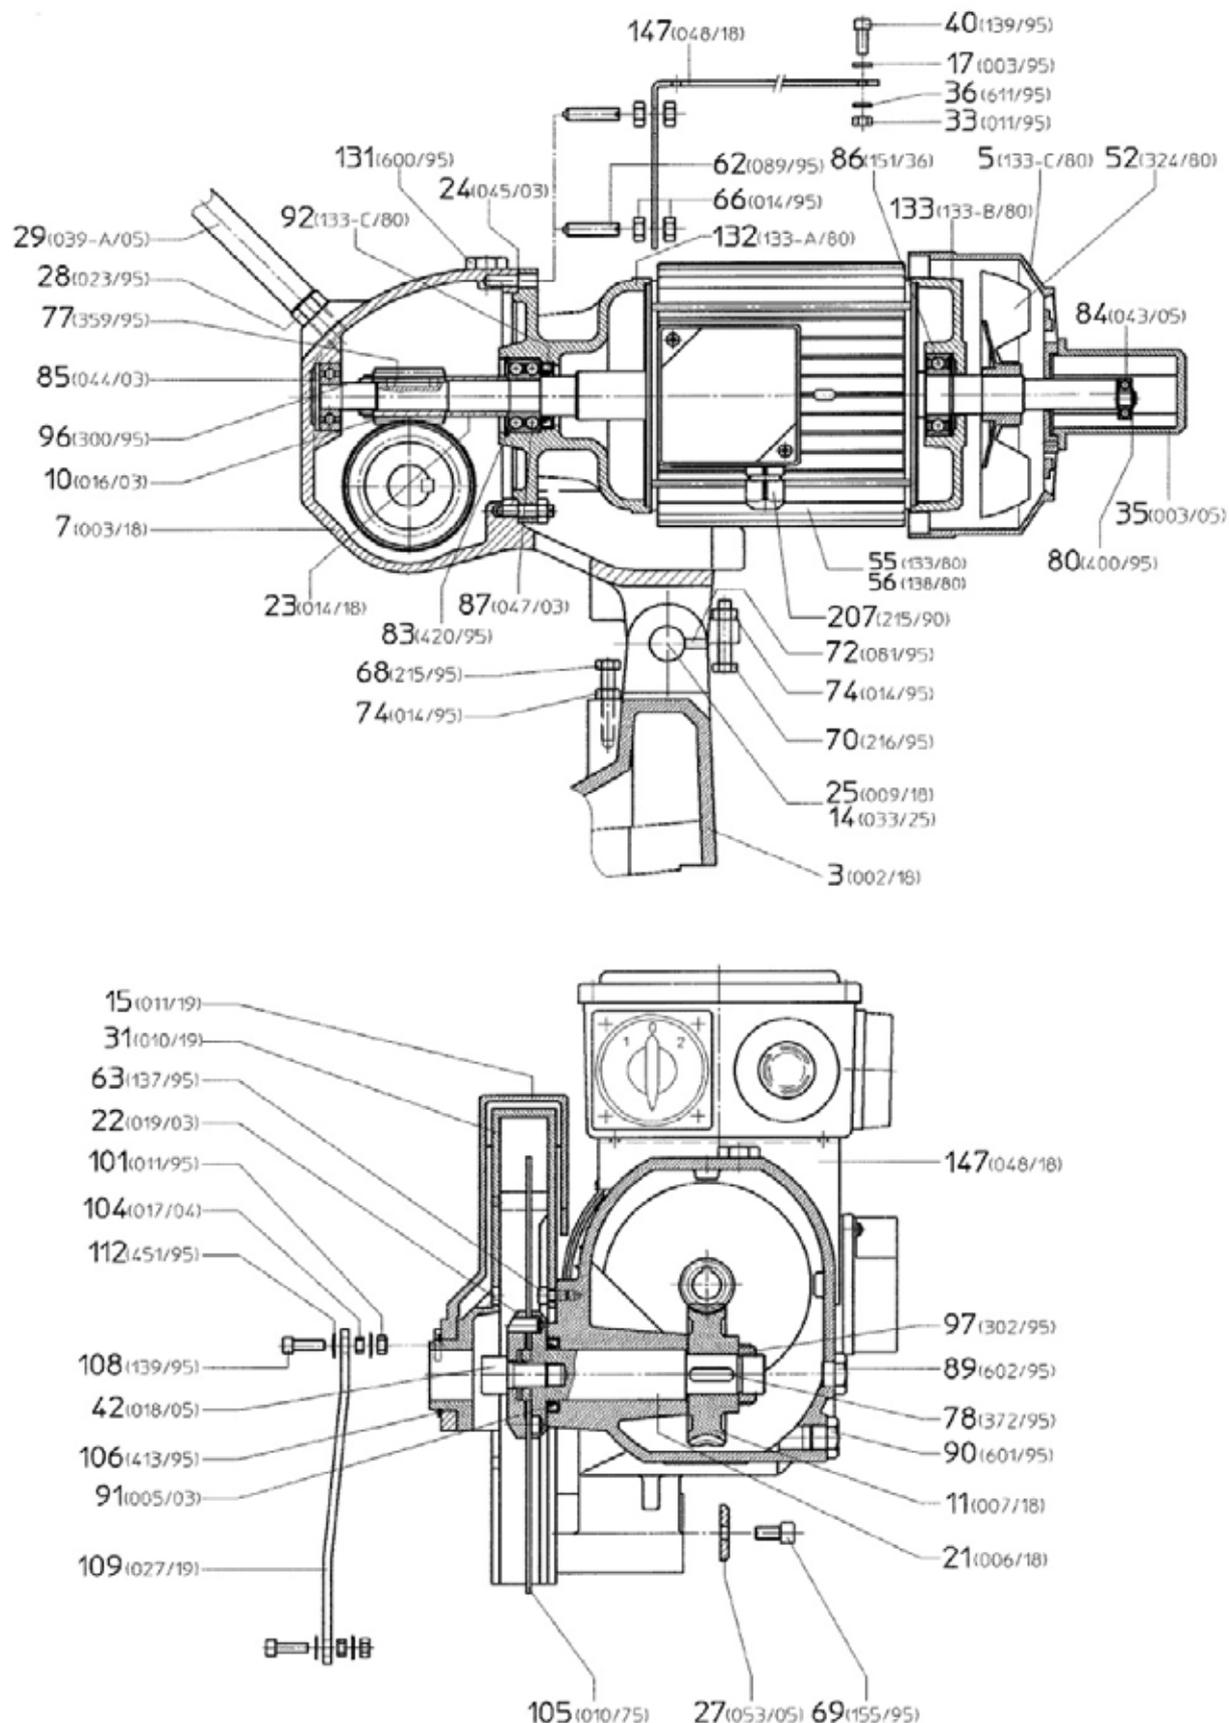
Dessin des pièces détachées 2 - MKS 275 N
